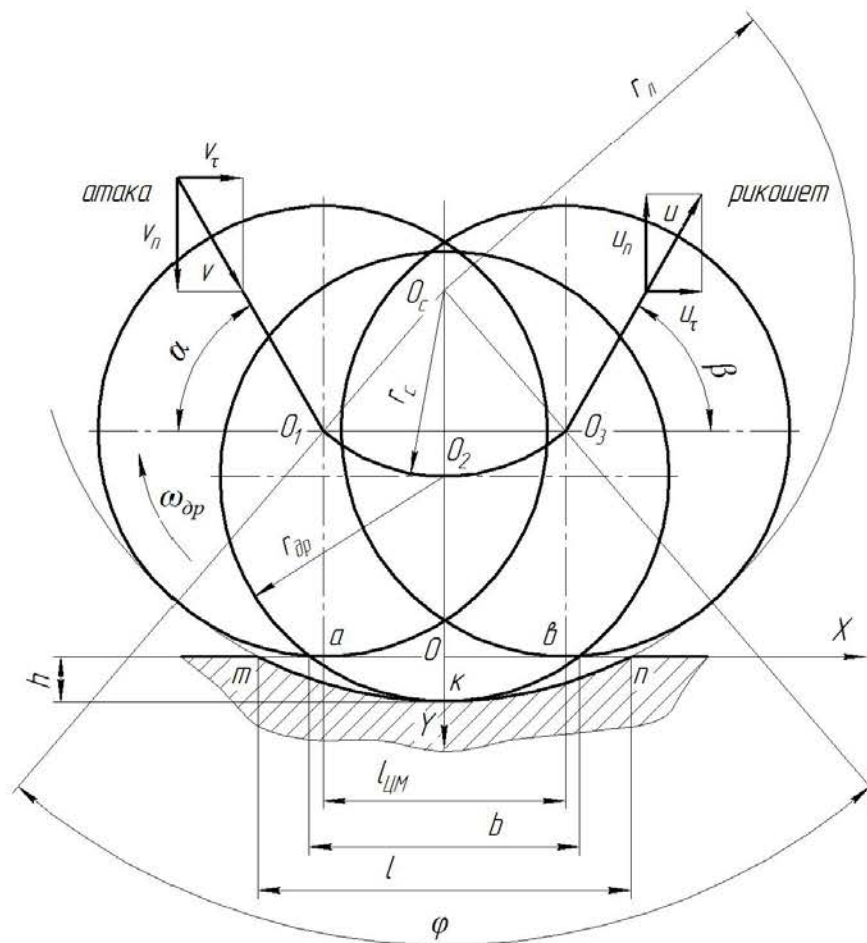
Схема взаємодії дробинки з металевою поверхнею
